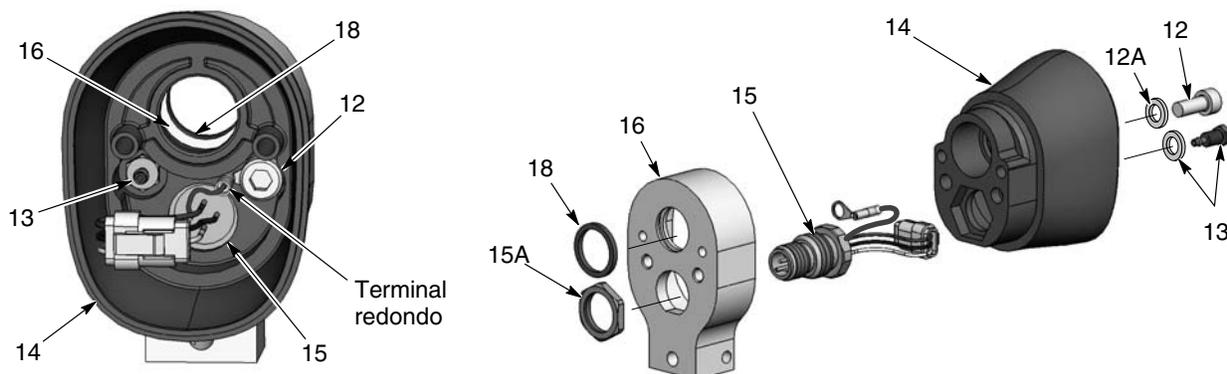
Desmontagem de pistola com barra de suporte 3 de 3
